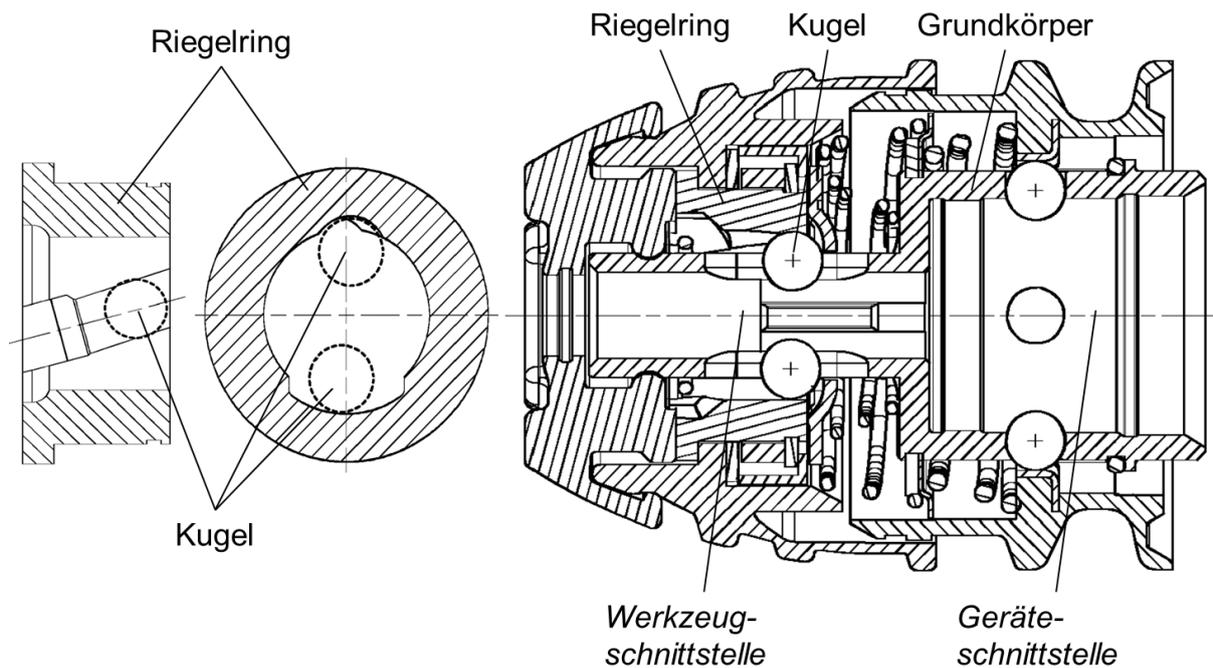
Entwickelte Werkzeugaufnahme zum verbesserten Abstellen des Schlagwerks³²⁰
